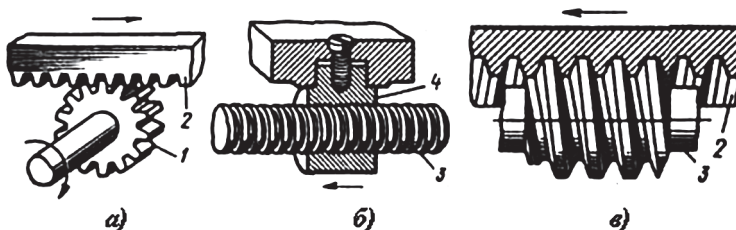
Зубчатые передачи для преобразования вращательного движения в поступательное:
